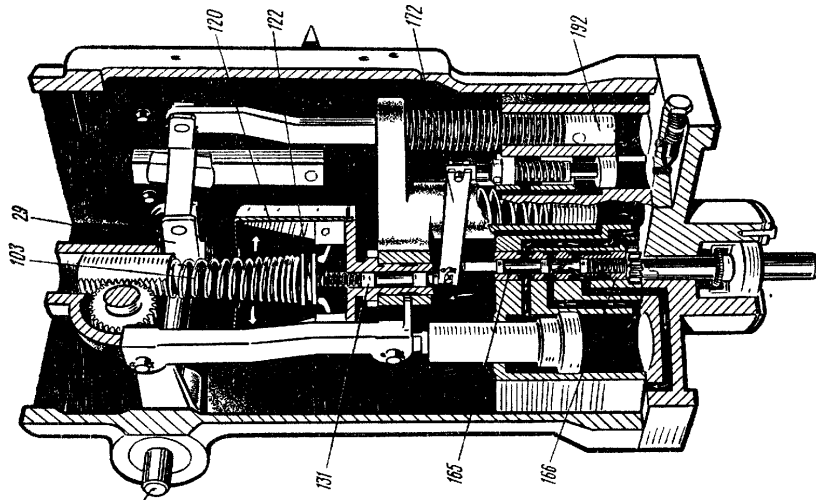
27 — выходной вал; 29 — рычаг изодрома; 103 — задающая пружина; 120 — муфта с подшипником; 131 — шток; 165 — распределительный золотник; 166 — втулка распределительного золотника; 172 — плавающий рычаг; 192 — принимающий поршень изодрома
